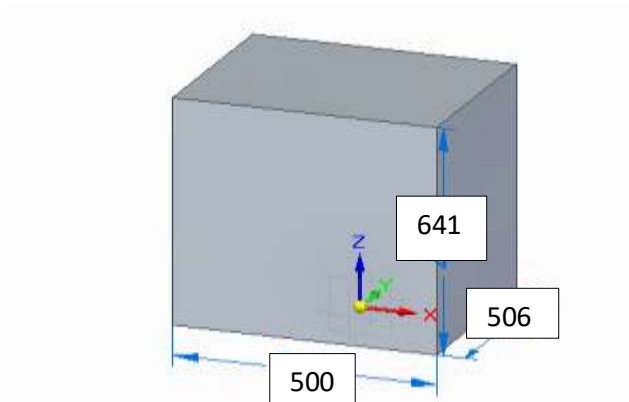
Dibujo de las dimensiones en mm del tanque (solid Edge ST10).
